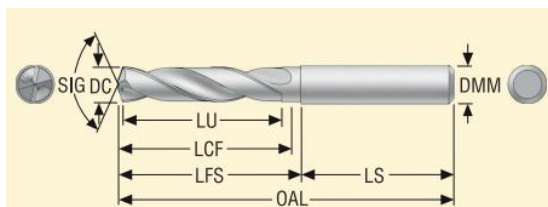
Свердло SD1103-0900-035-10R1 [2, с. 28]
